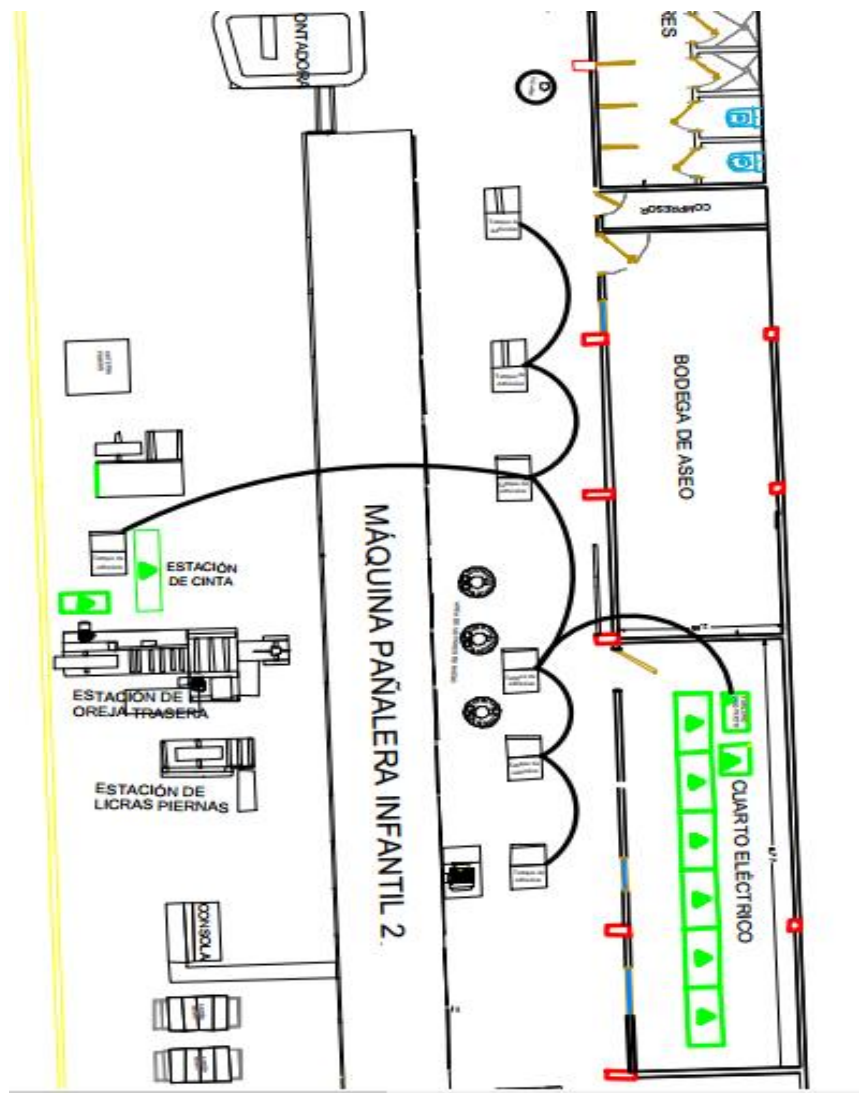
Plano de Máquina y Ubicación de los Tanques.
